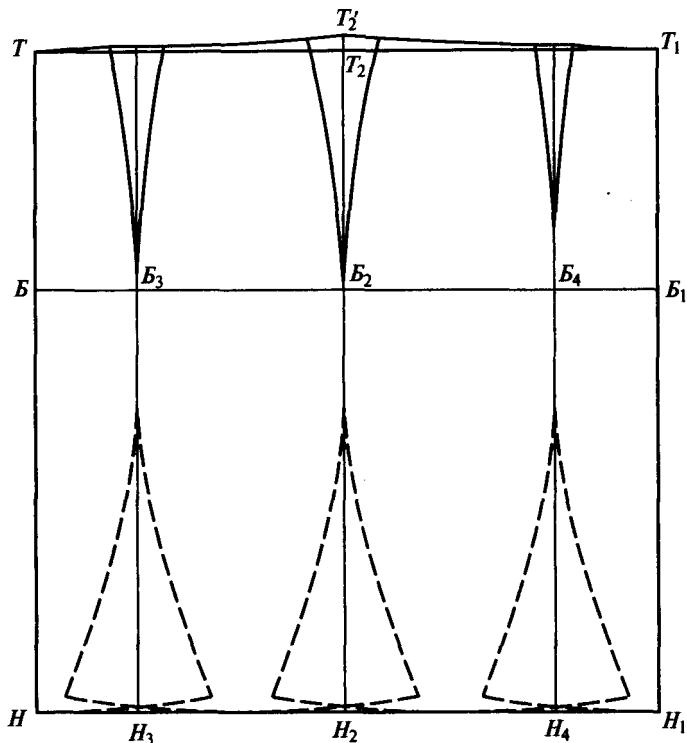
Чертеж основы конструкции юбки из шести клиньев
